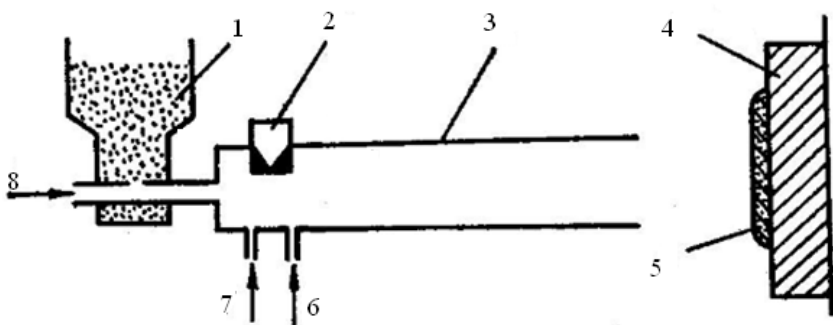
Схема детонаційно-газового пристрою для напilenня покриттів: 1 – бункер з порошком та пристроєм для дозування; 2 – свічка запалювання; 3 – робочий канал; 4 – виріб для обробки; 5 – покриття; 6 – горюча суміш; 7 – флегматизуючий газ; 8 – транспортуючий газ
